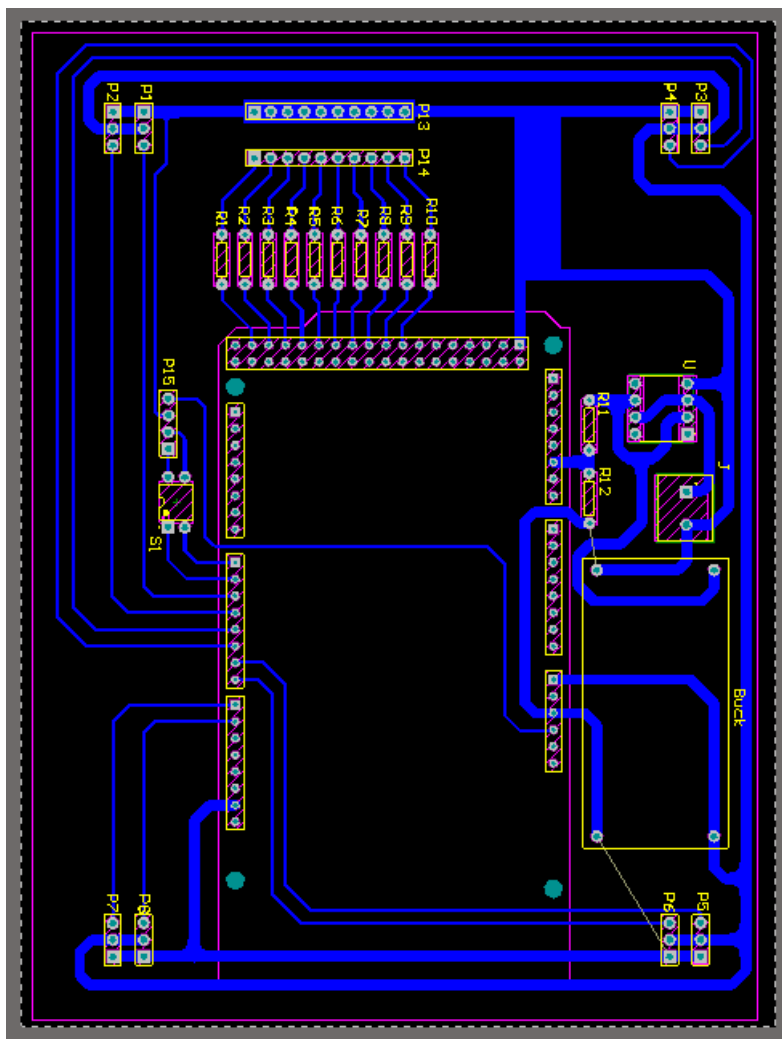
Vista de Diseño del PCB creado para interfazar todos los componentes del robot
